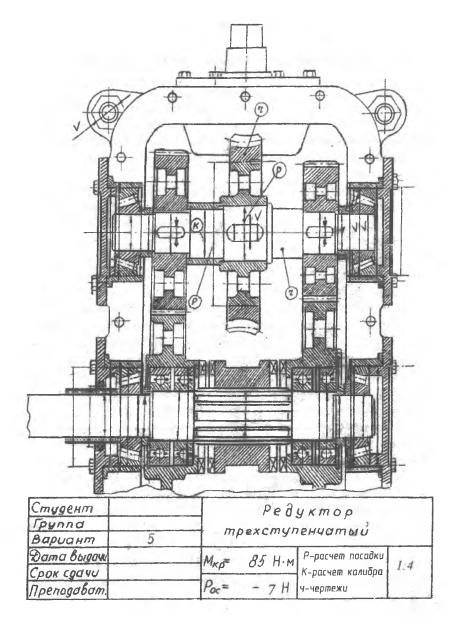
Задание на курсовую работу (сборочный чертеж редуктора)
